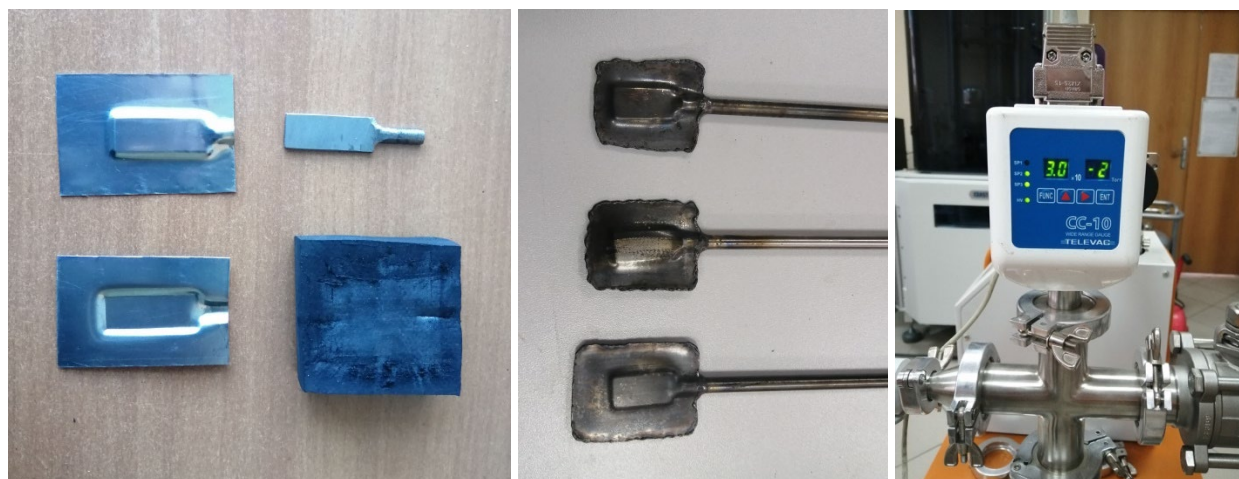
Штампованные заготовки контейнеров из нержавеющей стали, контейнеры с образцами, герметизированные аргонно-дуговой сваркой, и вакуумная система
